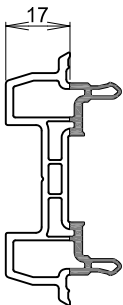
Zuschnitt und Bearbeitung Einlaufprofil 76654
